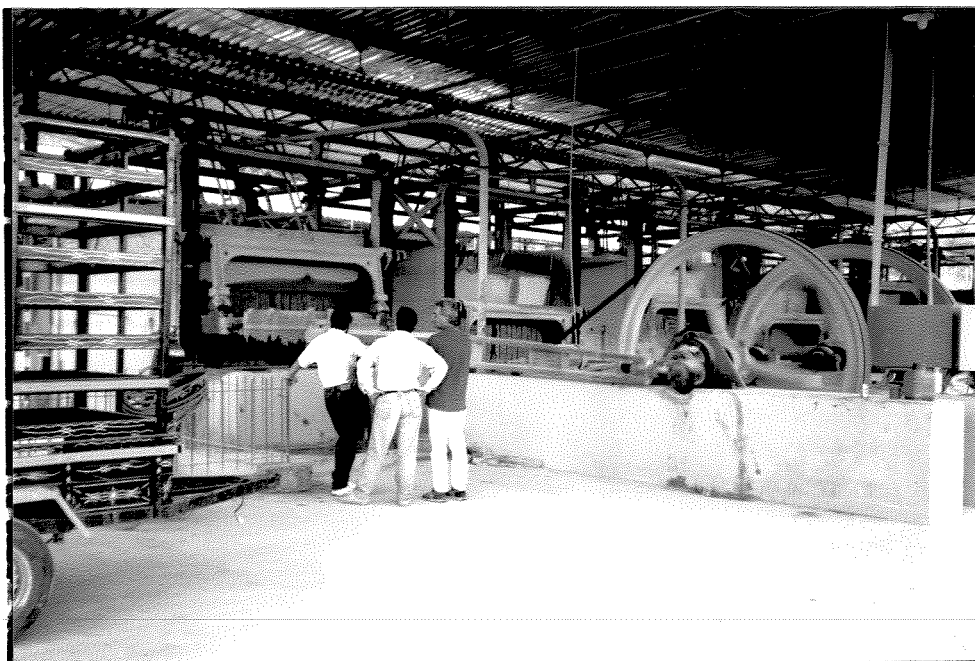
Corte de Blocos de Granito para Produção de Chapas Utilizando Tear de Lâminas
